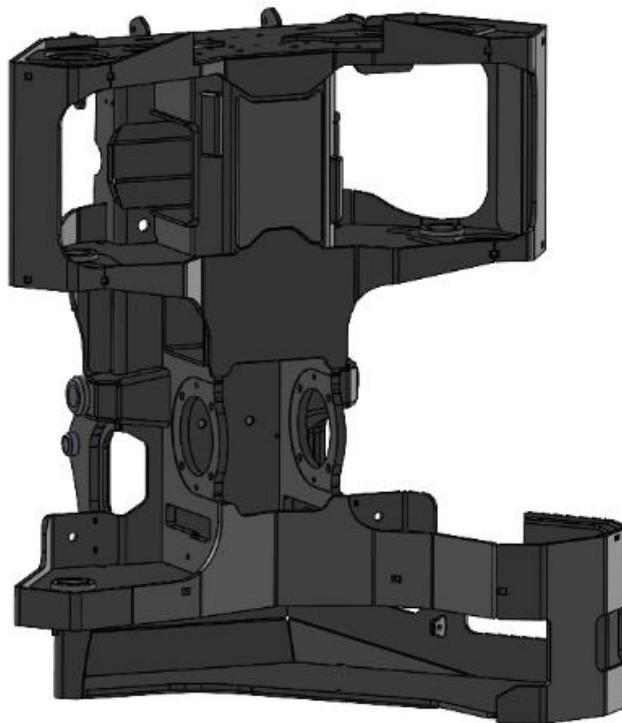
Chassi soldado da cabeça processadora V340HD.
